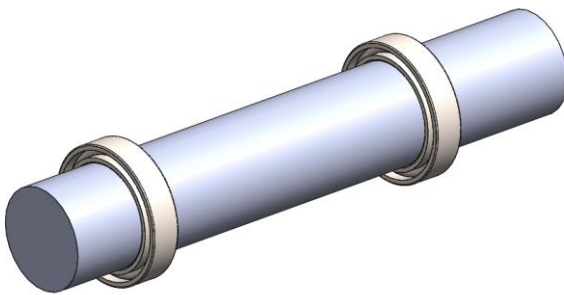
Diseño en Solid Works. Rodamientos 6203 instalados en una flecha
